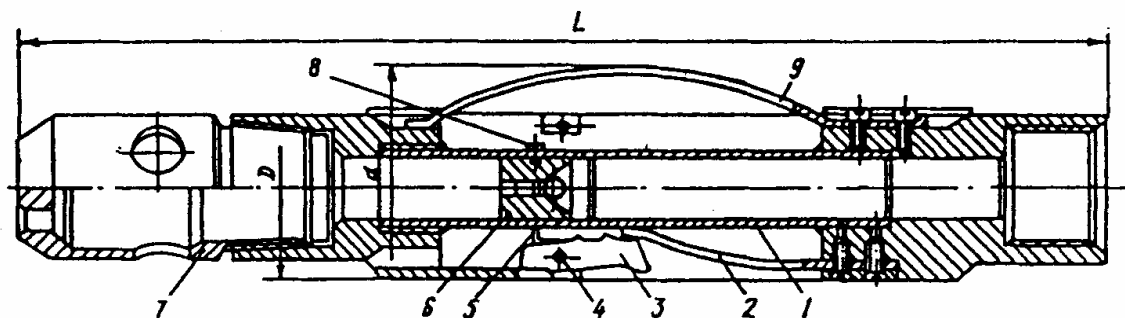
Скважинный механический фиксатор типа ФГМ
